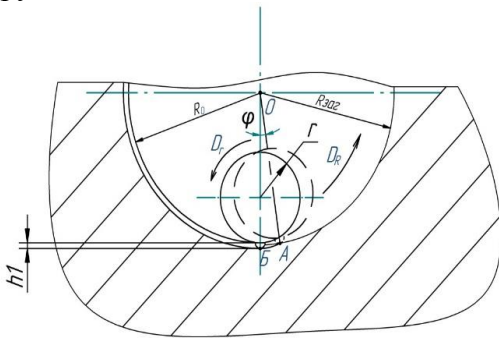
Схема кинематики планетарной обработки отверстий в деталях
